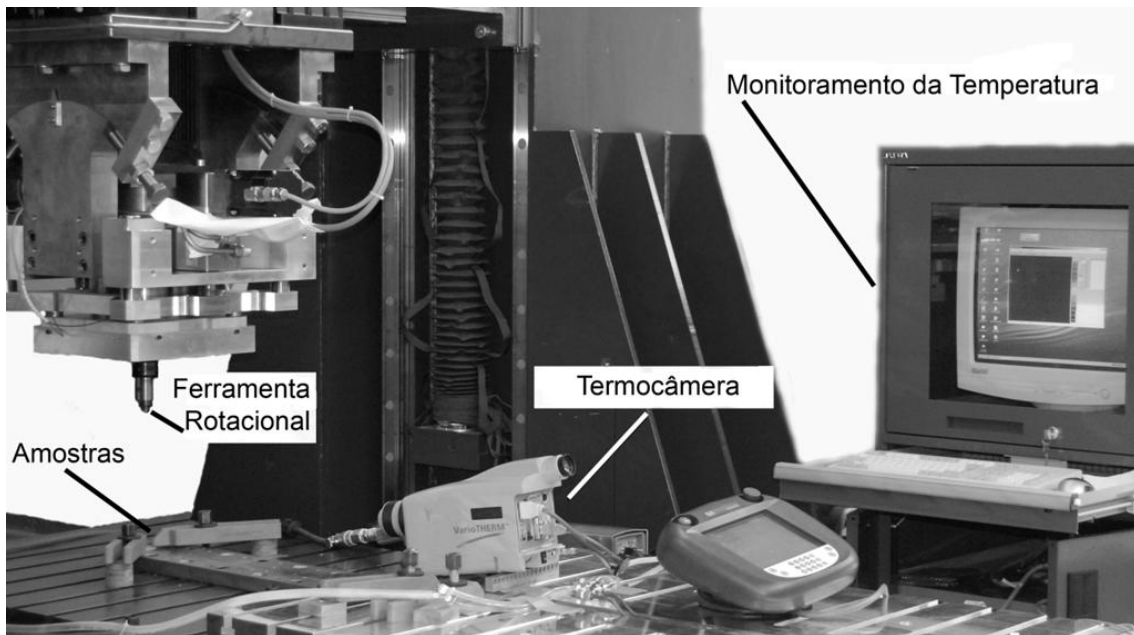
Equipamentos utilizados durante a soldagem por FSSW.
